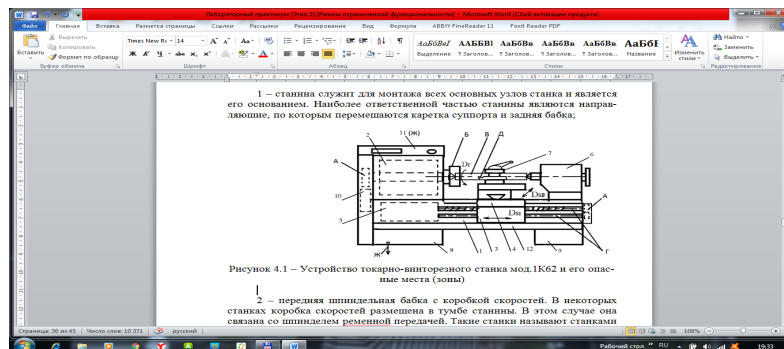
Устройство токарно-винторезного станка мод.1К62 и его опасные места (зоны)
